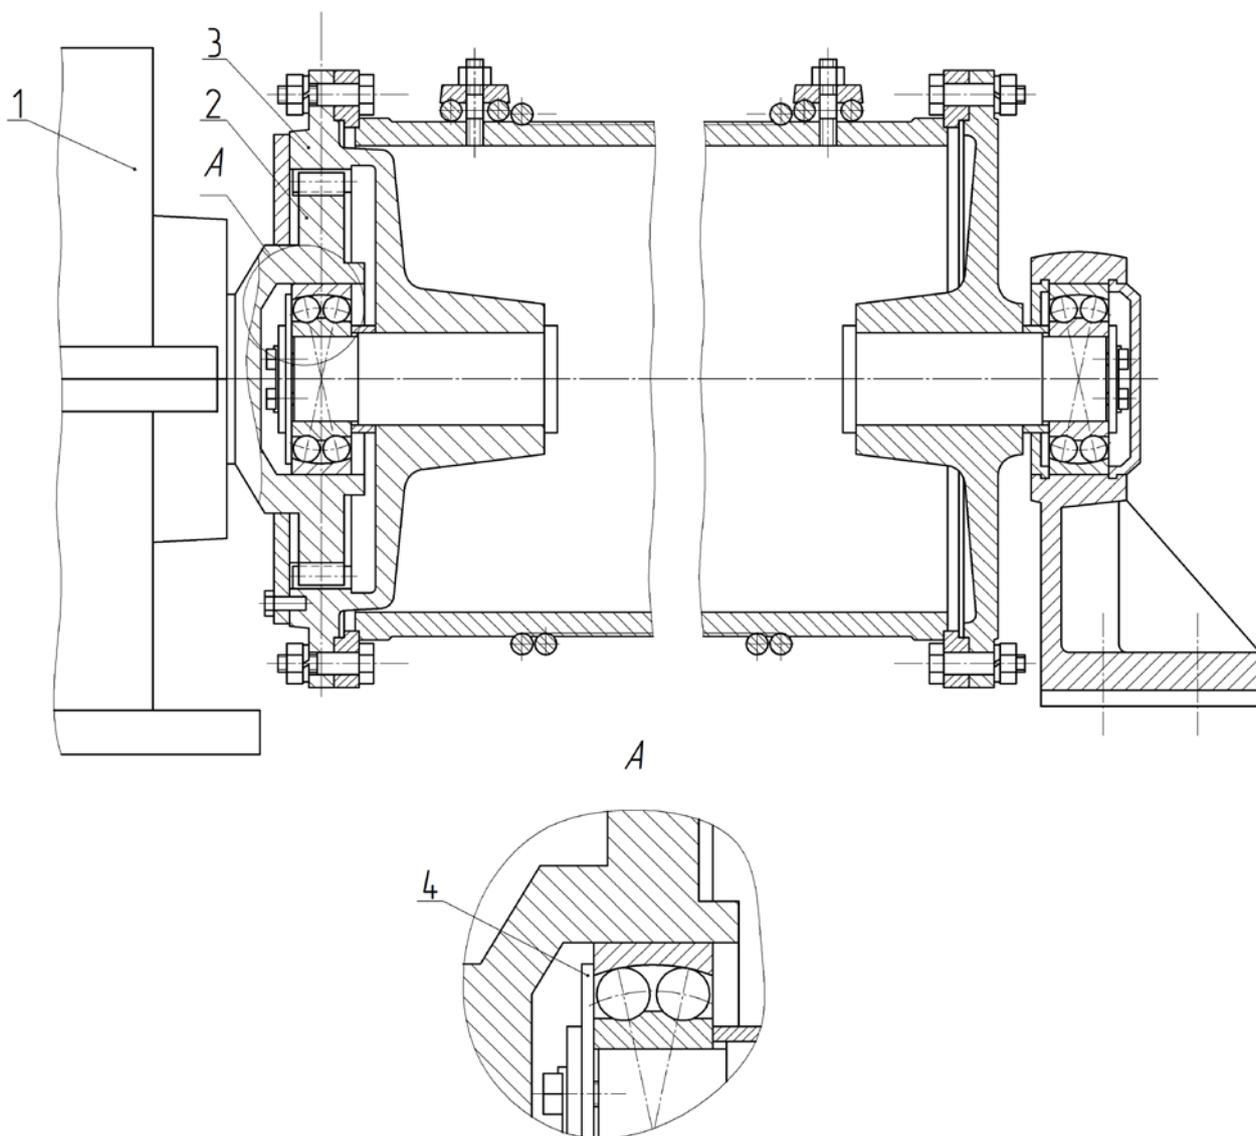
Соединение редуктора с барабаном при помощи зубчатой муфты: 1 – редуктор; 2 – зубчатый венец на конце тихоходного вала редуктора; 3 – полумуфта на канатном барабане с внутренними зубьями; 4 – шайба
